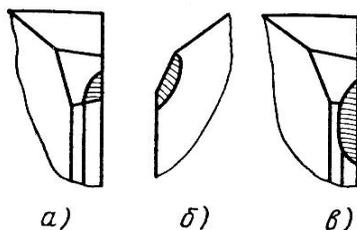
Схема износа развёртки из быстрорежущей стали:
